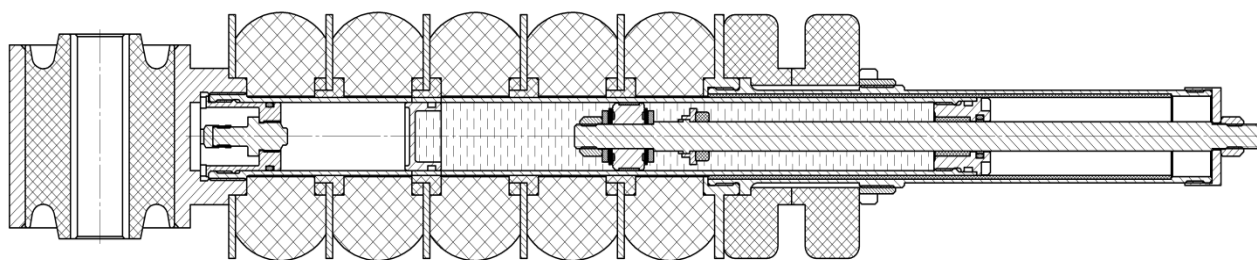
Схема гидроэластомерного пакета подвески автомобиля
